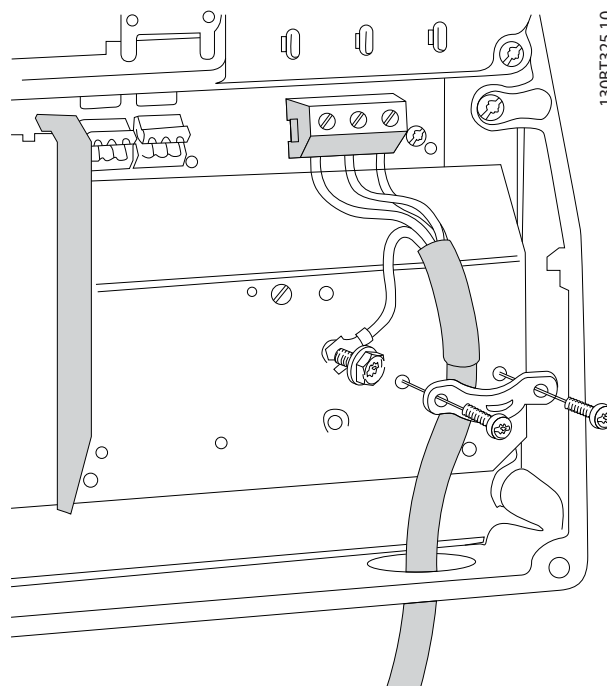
IP54, размеры корпуса I2, I3, I4
